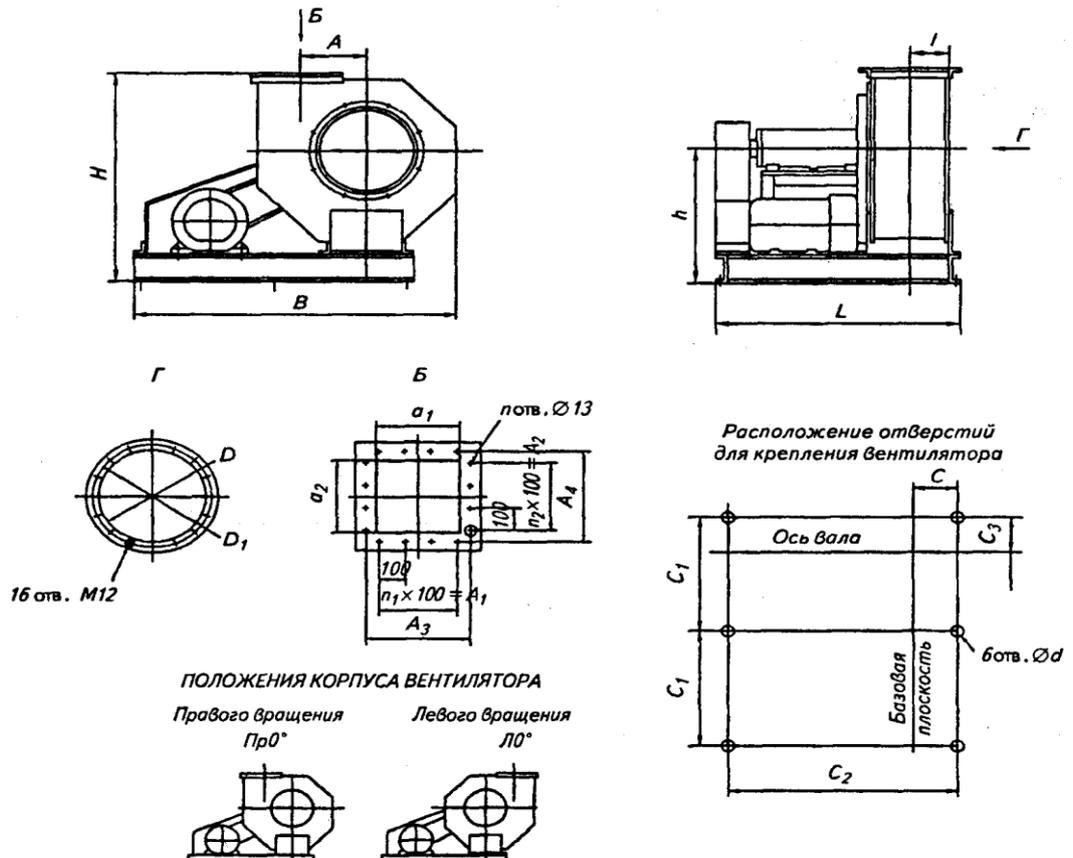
Габаритные и присоединительные размеры вентиляторов ВР-100-45
